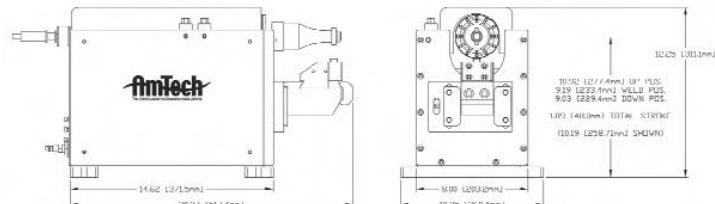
Verwendete Ultraschallschweißanlage (Ultraweld®- L20) [58]
